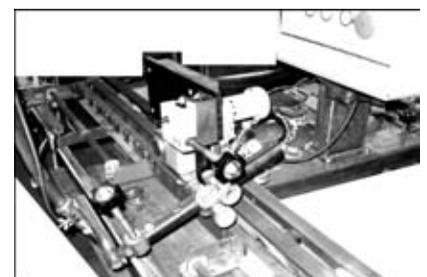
Автомат для многослойной сварки алюминиевых конструкций
